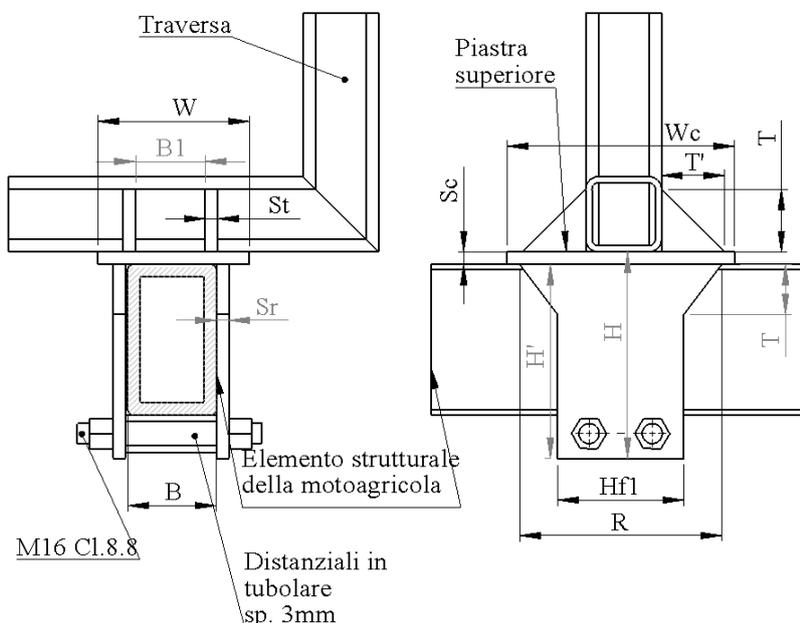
Dimensioni e ingombri degli elementi principali del dispositivo di attacco di classe  $C_2$  a Collegamento Verticale con giunto flangiato.
